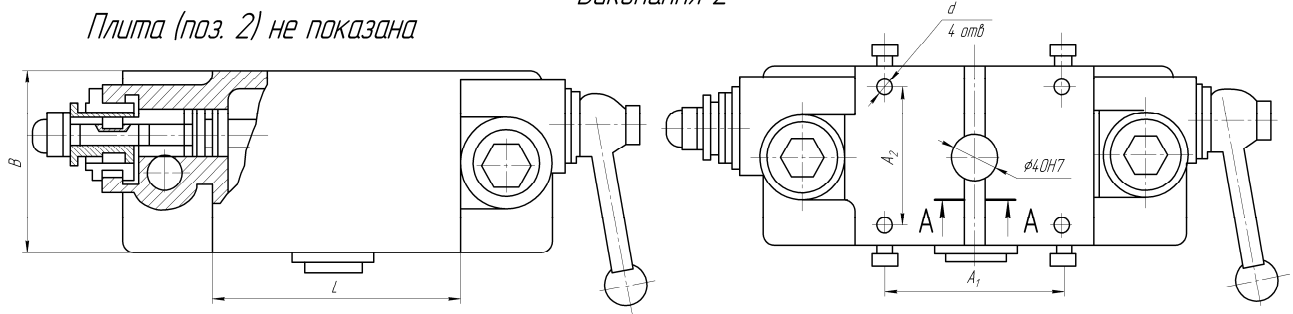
Будова й параметри кондуктора скальчастого порталного з конусним затискачем (ГОСТ 16891-71): 1 – корпус; 2 – плита; 3 – рукоятка
